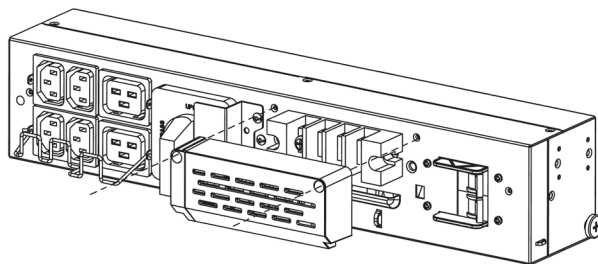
Extracción cubierta terminales de la parte frontal del BM-R.
